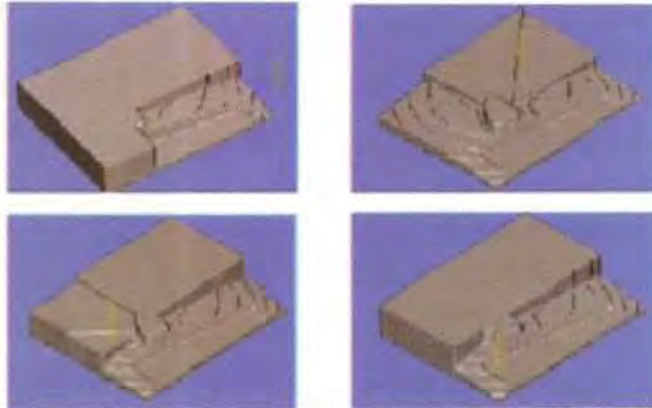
Muestra de las cuatro etapas en las que se ha dividido la fase de desbaste
